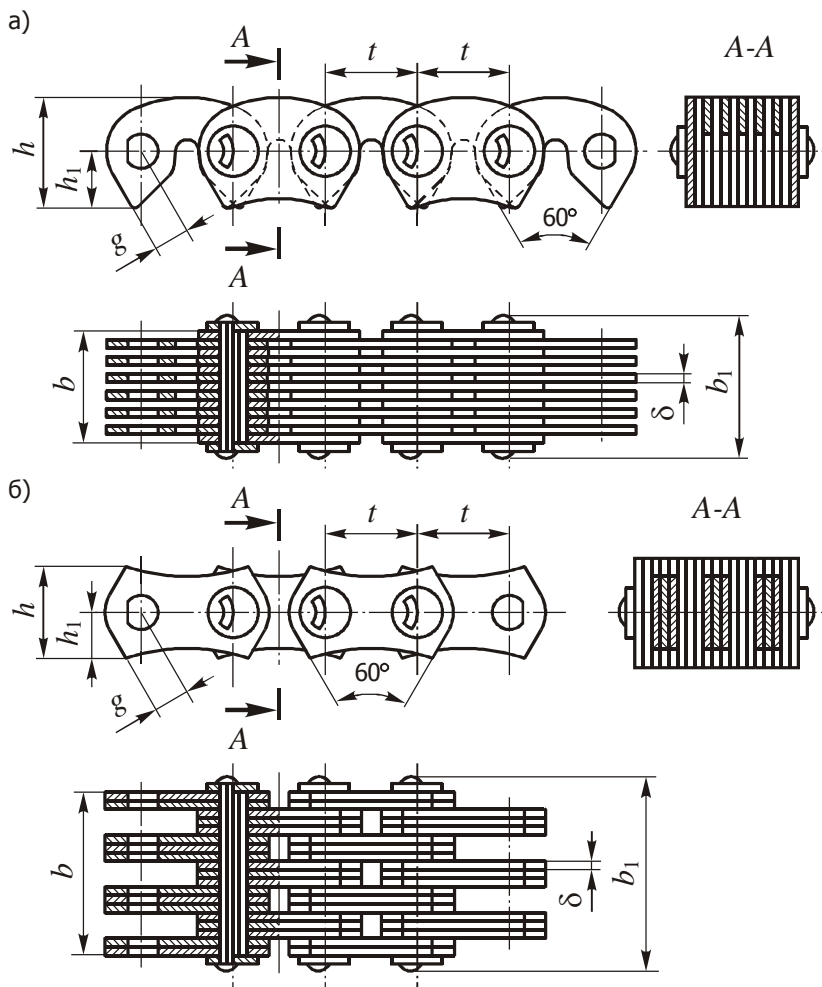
Конструкция зубчатых цепей: а – цепь типа 1; б – цепь типа 2
